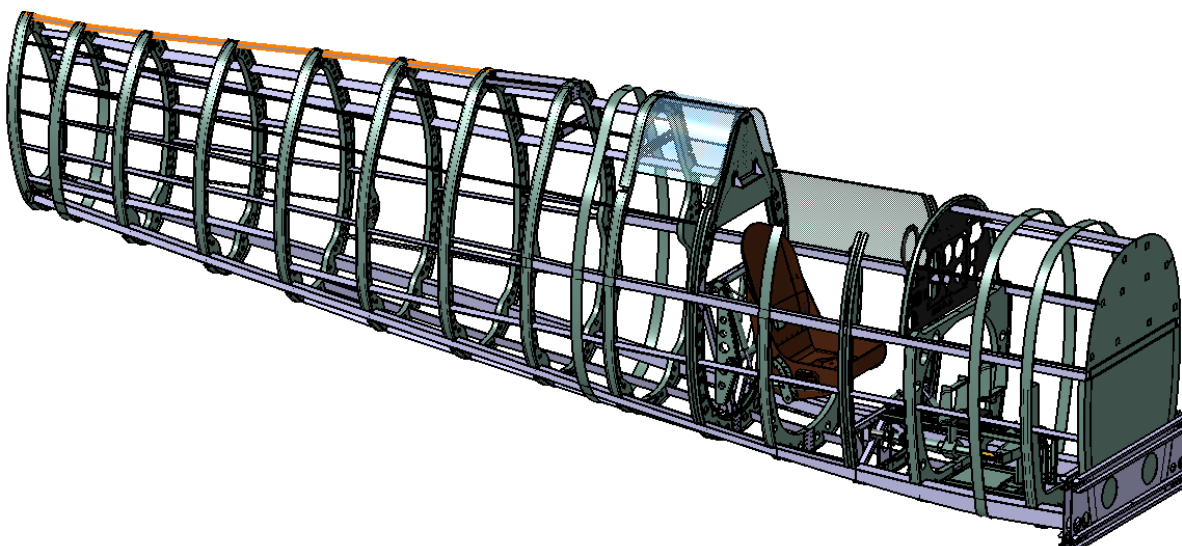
Larguero superior principal en el entorno del fuselaje
